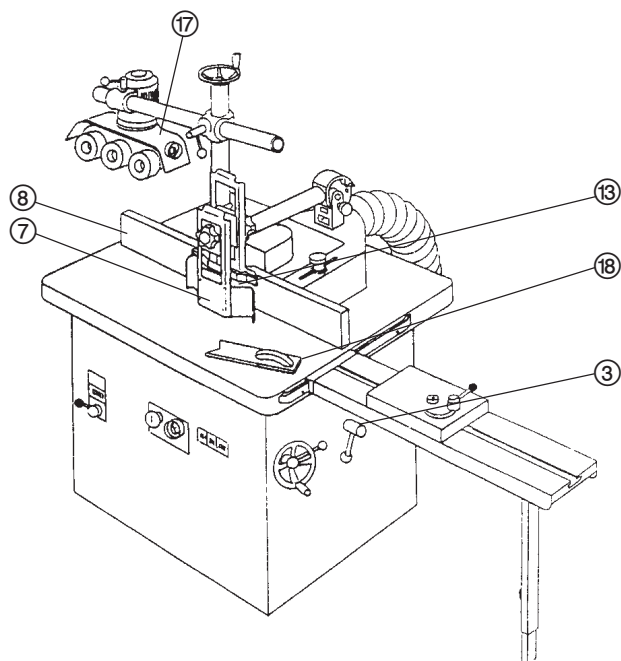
Einspindelige senkrechte Tischfräsmaschine ausgerüstet zum Fräsen am Anschlag
